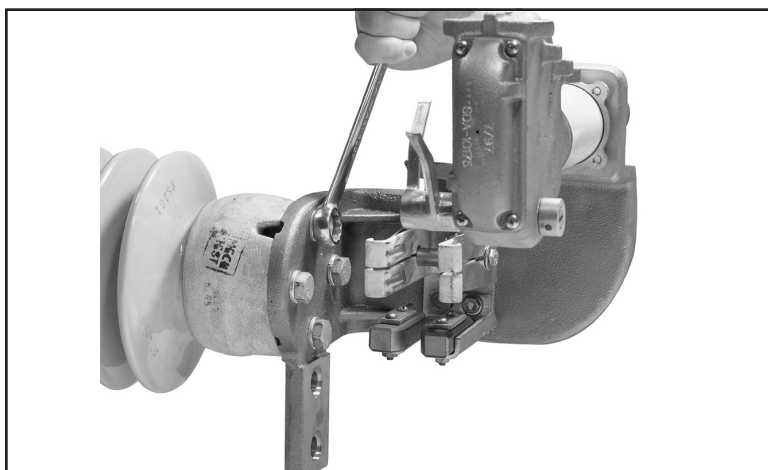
Colocando la pieza fundida de reemplazo de la base terminal con calzadores instalados.
